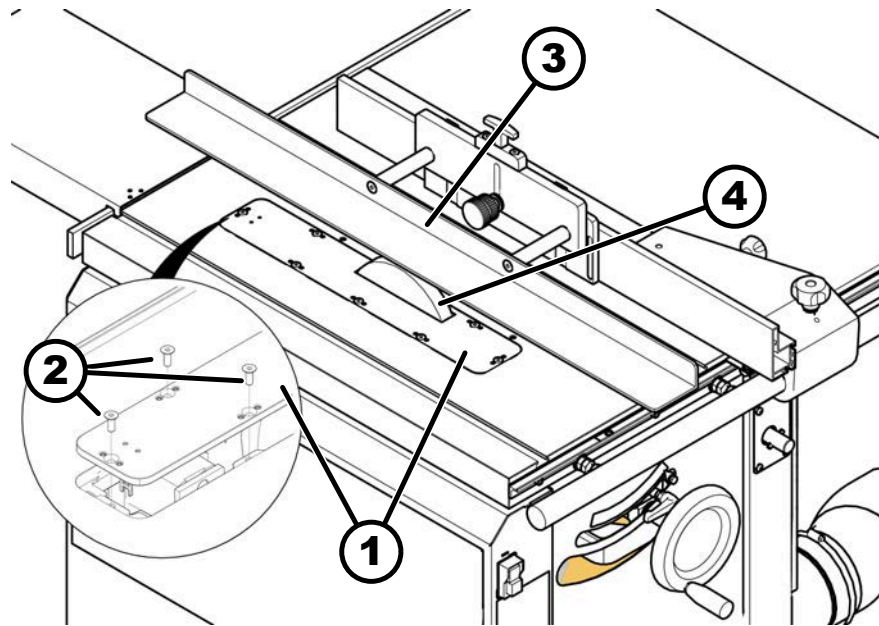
Betriebsbereitschaft - Nutwerkzeuge
